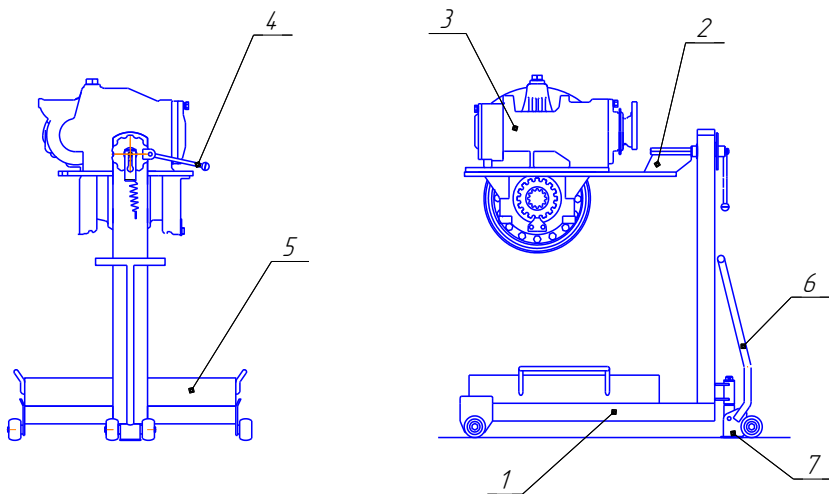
Эскиз стэнда для ремонта редукторов: 1- основание; 2 – кронштейн; 3 – редуктор; 4 – рычаг фиксатора; 5 – ванна; 6 – ручка транспортная; 7 – пята.
